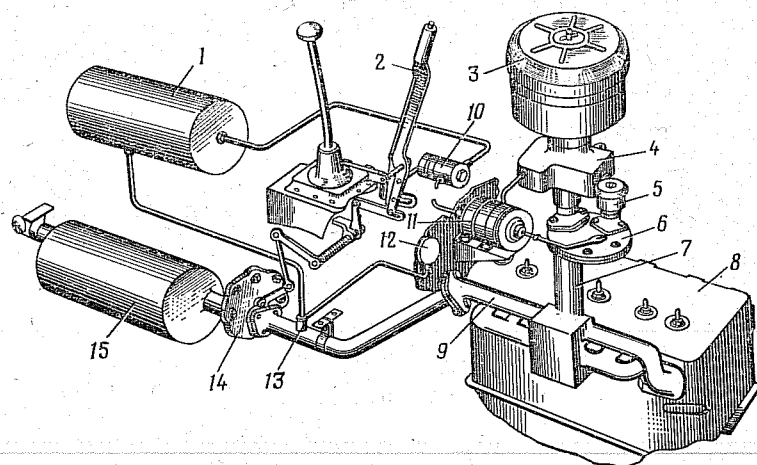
Схема монтажа замедлителя на карбюраторный двигатель: 1 — воздухохраник; 2 — рычаг управления замедлителем; 3 — воздухоочиститель; 4 — карбюратор; 5 — воздушный фильтр; 6 — механизм отключения карбюратора; 7 — впускная труба; 8 — двигатель; 9 — выпускная труба; 10 — кран управления; 11 — рабочий цилиндр; 12 — манометр; 13 — редукционный клапан; 14 — заслонка выпускной трубы; 15 — глушитель
